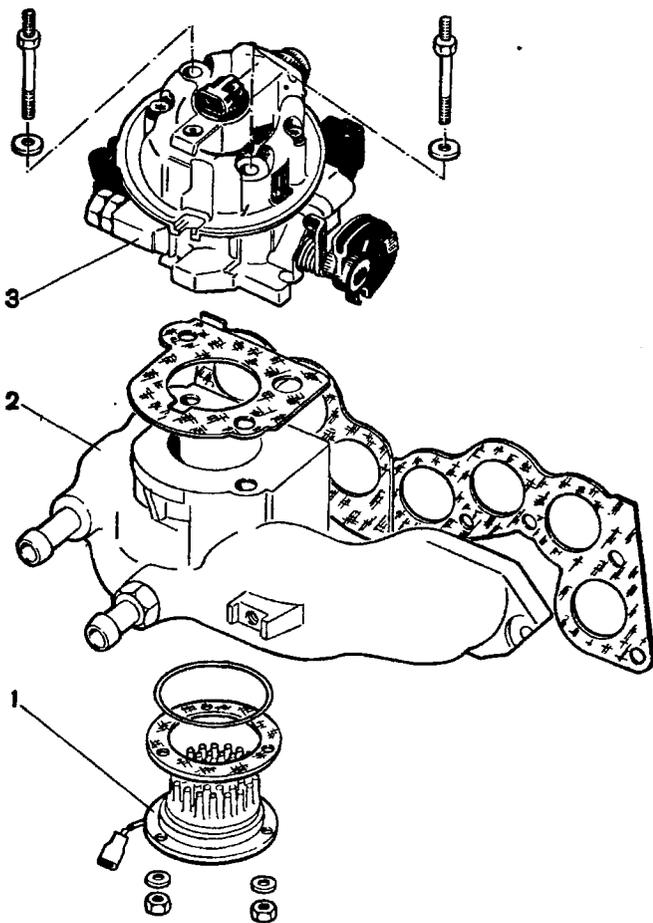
Снятие агрегата центрального впрыска топлива и впускной трубы: 1 - подогреватель впускной трубы; 2 - впускная труба; 3 - агрегат центрального впрыска
